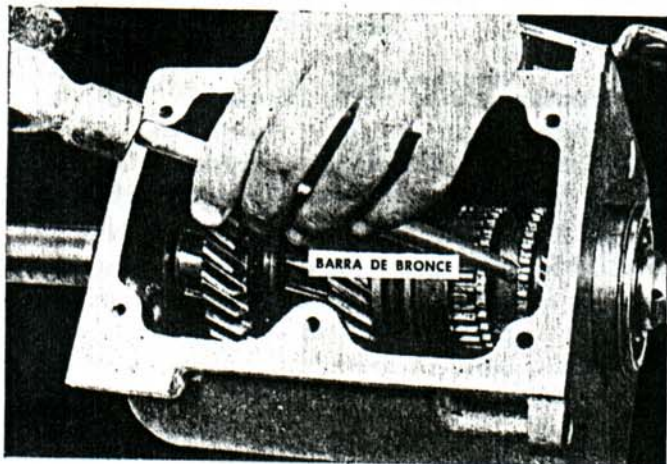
Extrayendo el engranaje de mando. Caja importada para "Carabela".
